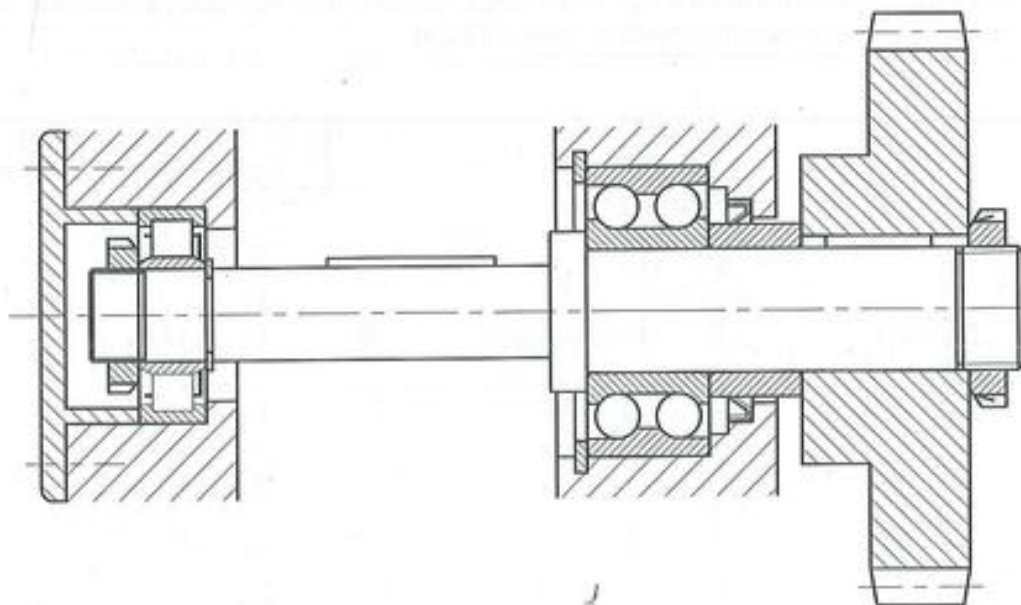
Disposición de rodamientos. Rodamiento de rodillos cilíndricos sin pestaña en aro interior, libre a la izquierda y rodamiento fijo a la derecha.
